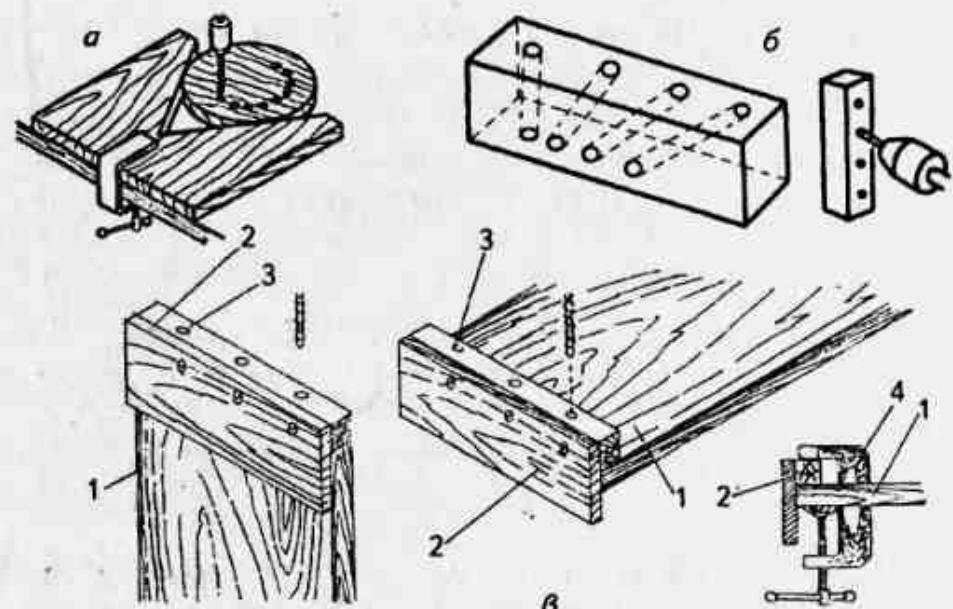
Приспособления для сверления древесины: а — применение упора для сверления отверстий в круглых заготовках; б — применение упора для сверления отверстий в вертикальной плоскости; в — шаблон для сверления торца и плоскости заготовки: 1 — заготовка; 2 — шаблон; 3 — отверстия в шаблоне; 4 — струбцина, с помощью которой крепится шаблон
